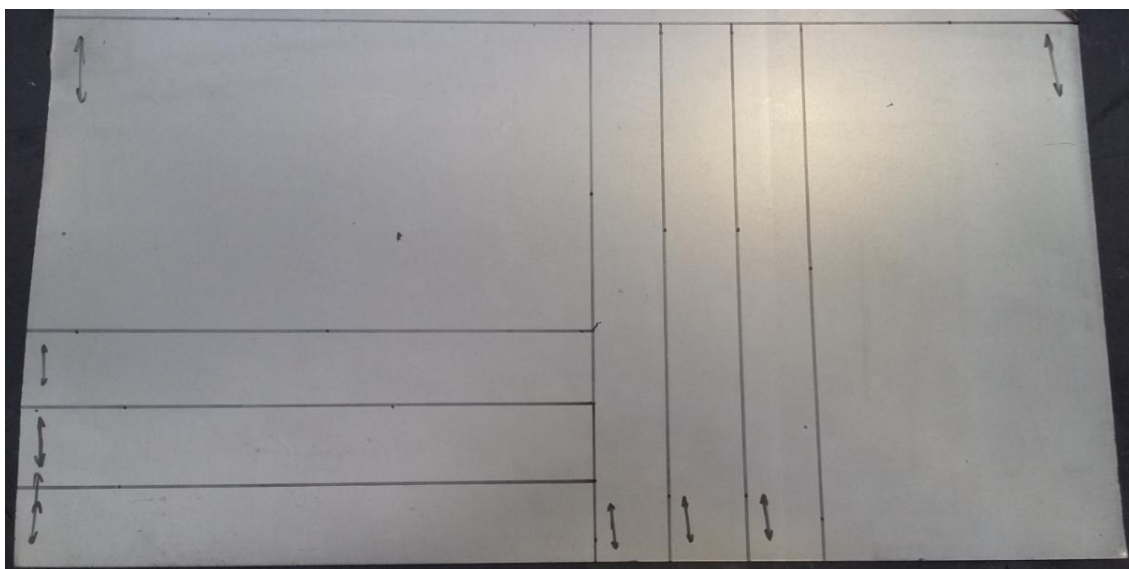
Probetas de acero marcadas para el ensayo de tracción.
